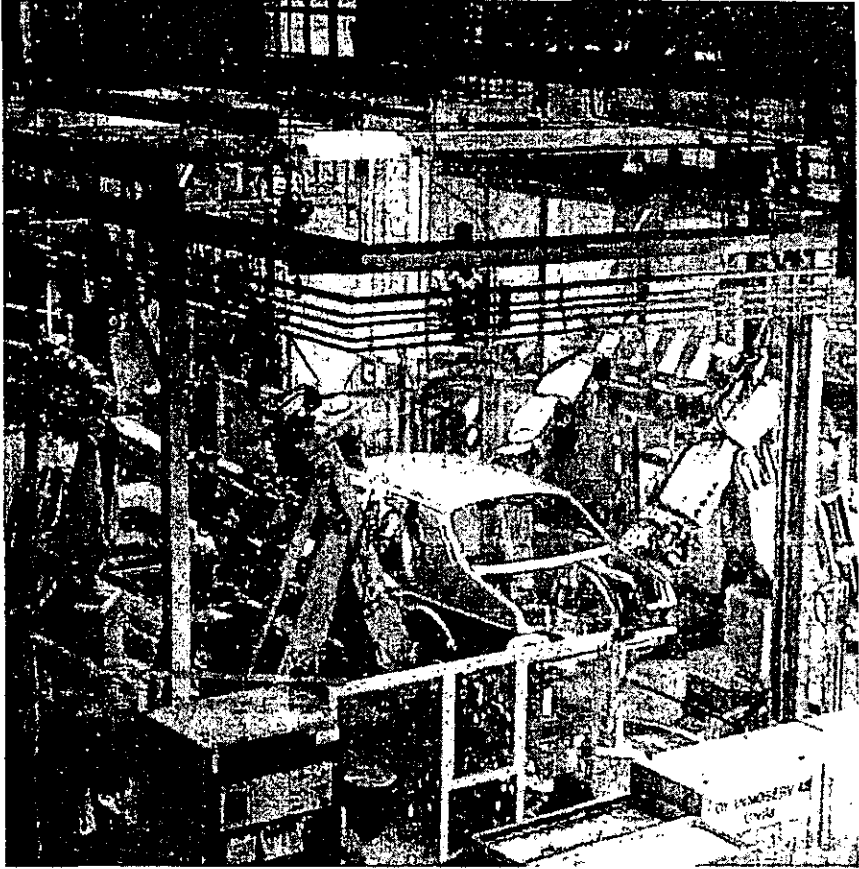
Sistema robótico industrial de soldadura de punto en SAAB, Suecia.
